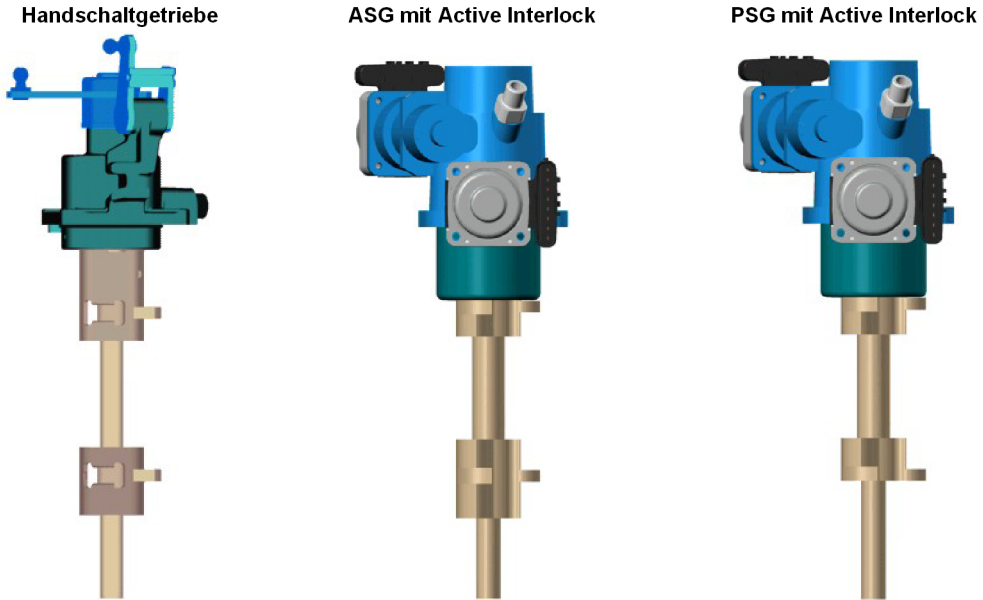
Betätigungsmodule für Handschalter, ASG und PSG
